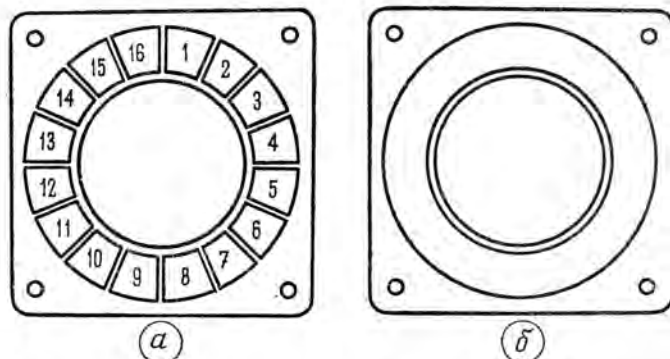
Плата коммутатора: а — вид сверху, б — вид снизу.
